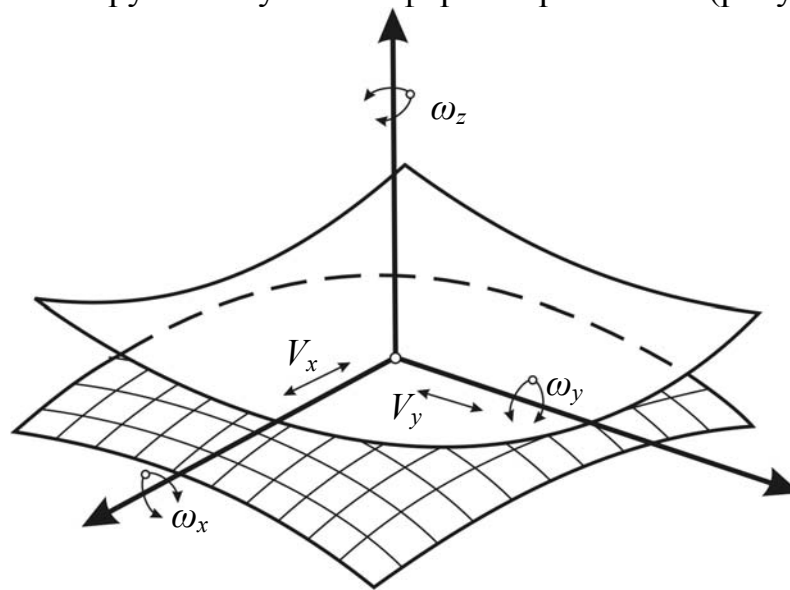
Общая принципиальная кинематическая схема многокоординатного формообразования поверхностей при механической обработке деталей
